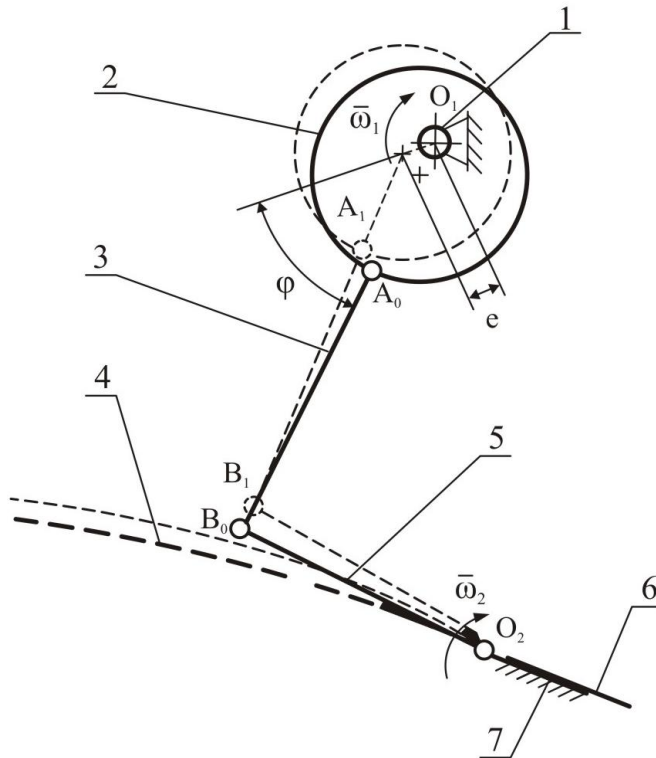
Кінематична схема приводу розпушувача плуга: 1 – приводний вал; 2 – ексцентрик; 3 – ексцентрикова тяга; 4 – розпушувач; 5 – важіль; 6 – викопувальна скоба; 7 – башмак.
